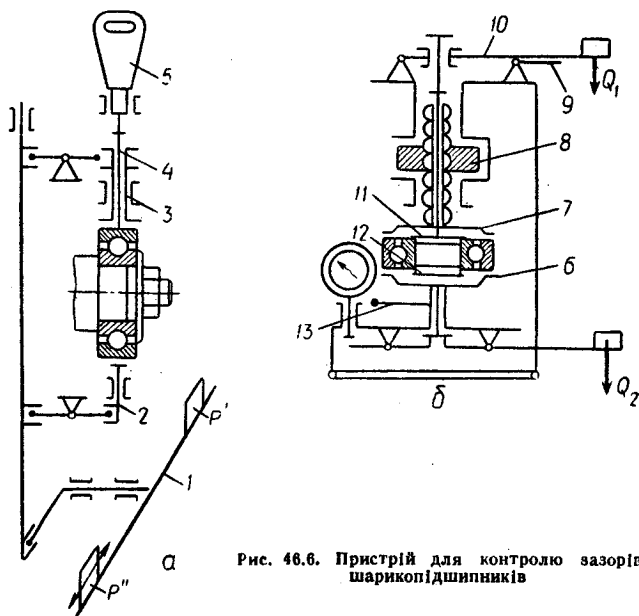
Пристрій для контролю зазорів шарикопідшипників
